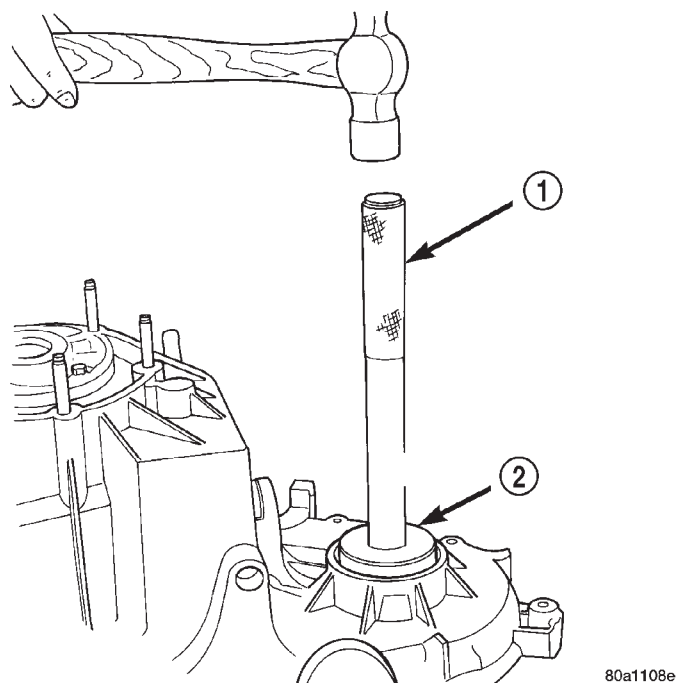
Desmontaje del cojinete del eje transmisor delantero
